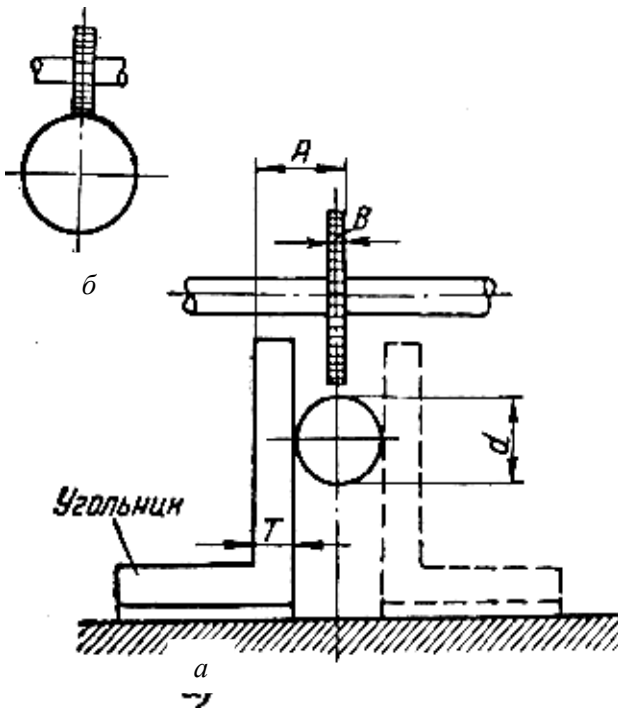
Проверка установки дисковой фрезы в диаметральной плоскости вала
